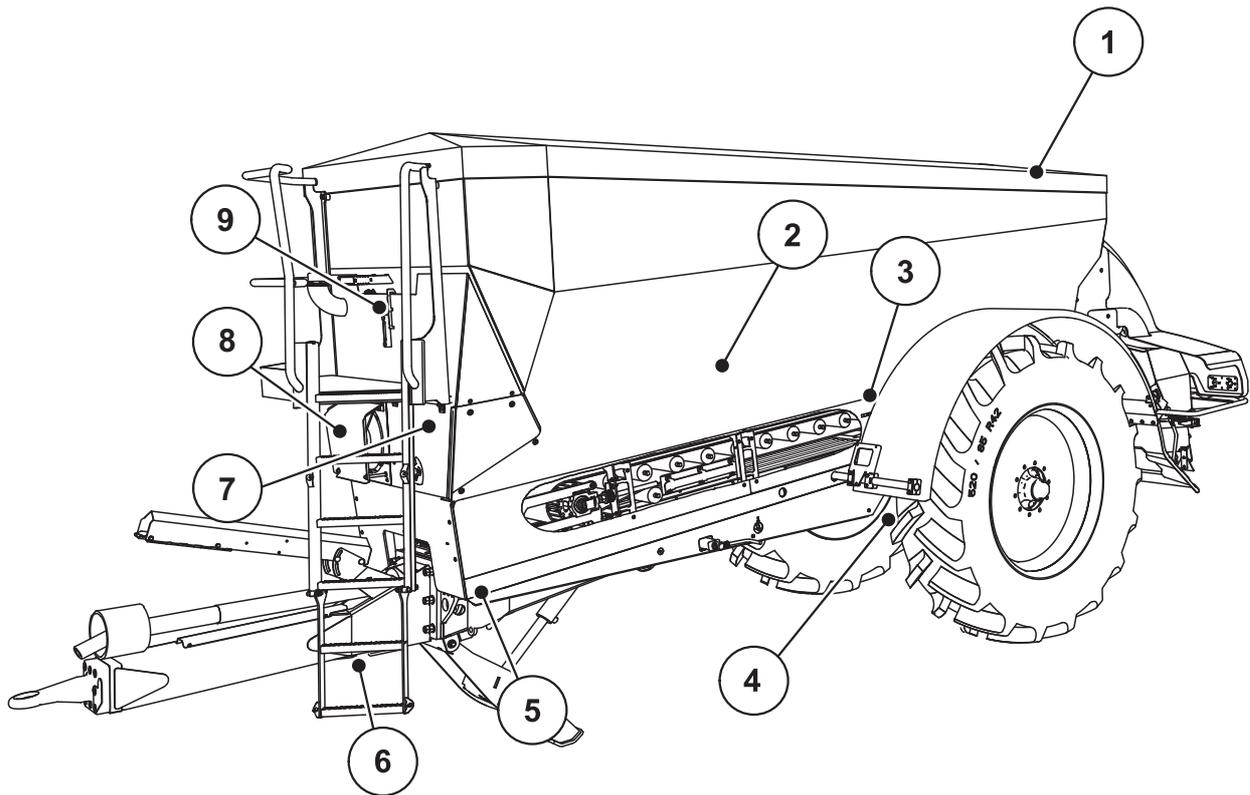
Vue d'ensemble des vérins et capteurs sur l'épandeur pour grandes surfaces AXENT
